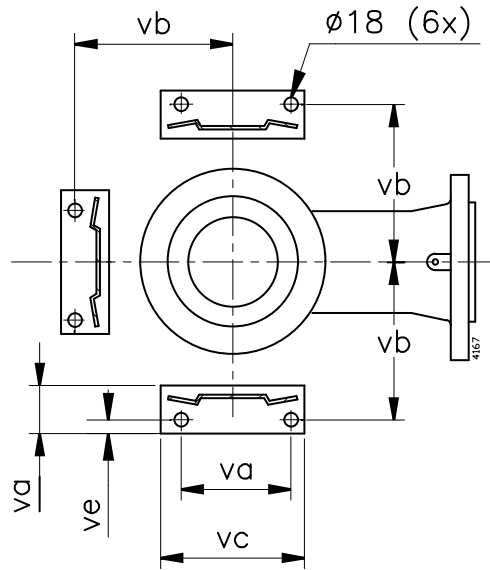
Размеры подкладок под стойки (вид сверху)
